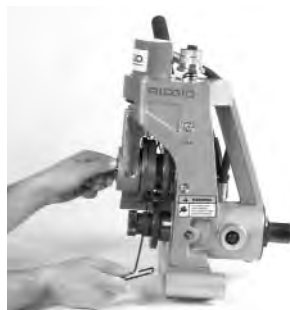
Desserrage de la vis de blocage des galets de rainurage
